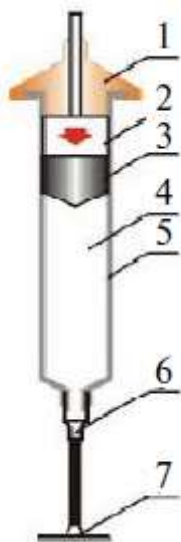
Схема нанесения припойной пасты на контактные площадки с помощью диспенсера: 1 – крышка; 2 – воздух под давлением; 3 – поршень; 4 – припойная паста; 5 – цилиндрический корпус; 6 – сопло; 7 – контактная площадка
